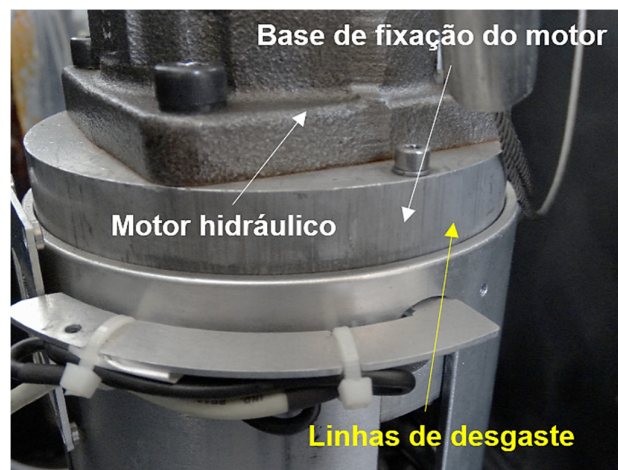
Desgaste por deslizamento causado na superfície externa da base de fixação do motor hidráulico.
